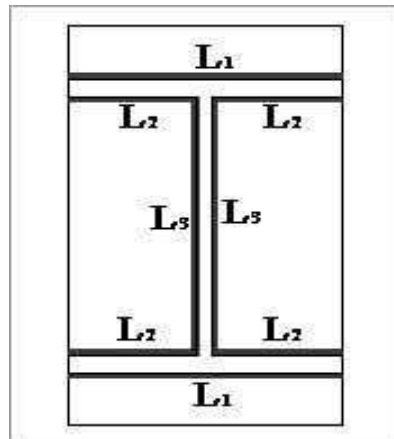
Dispositions de courdons de soudure (poutre platine)
